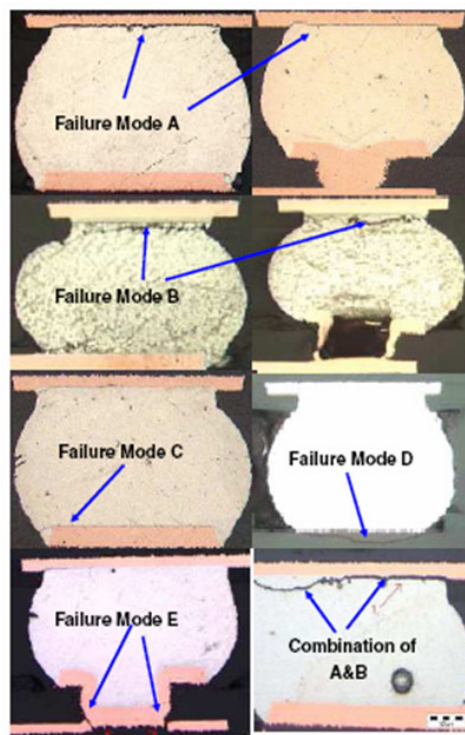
principaux modes de rupture des joints de soudure, observations expérimentales [12].
